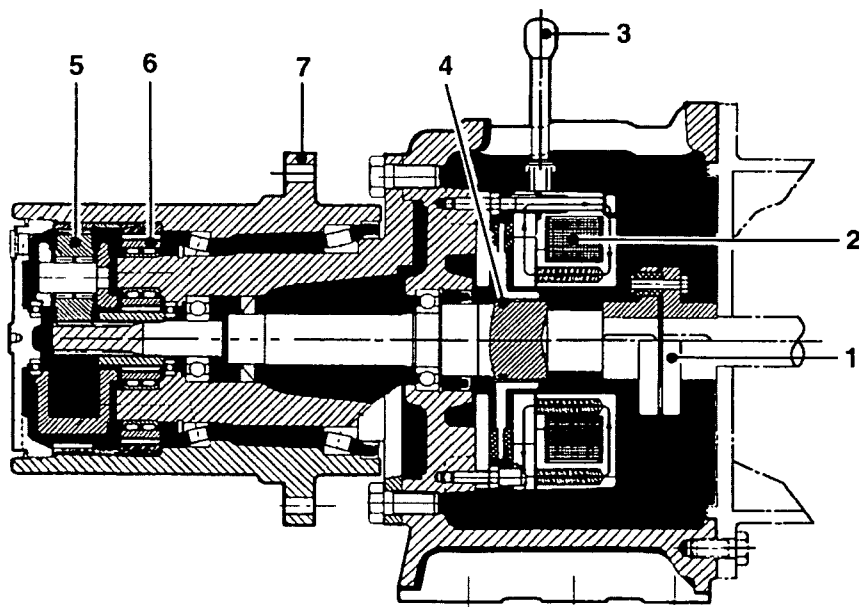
Конструктивная схема лебедки с двухступенчатой планетарной зубчатой передачей: 1 – соединительная упругая муфта, 2 – электромагнит дискового тормоза, 3 – ручной рычаг выключения тормоза, 4 – уплотнительное кольцо, 5 – первая ступень зубчатой передачи, 6 – вторая ступень зубчатой передачи, 7 – фланец крепления шкива
